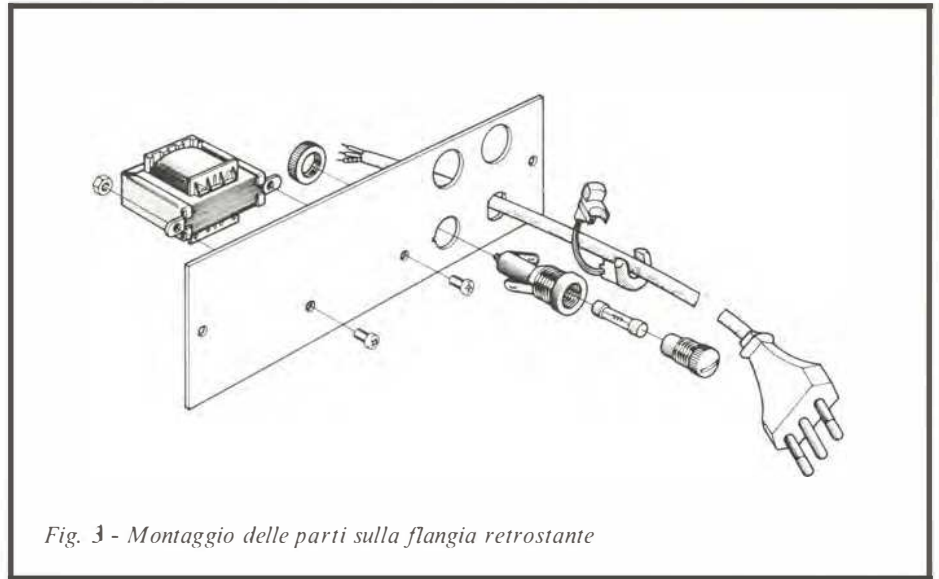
Montaggio delle parti sulla flangia retrostante
